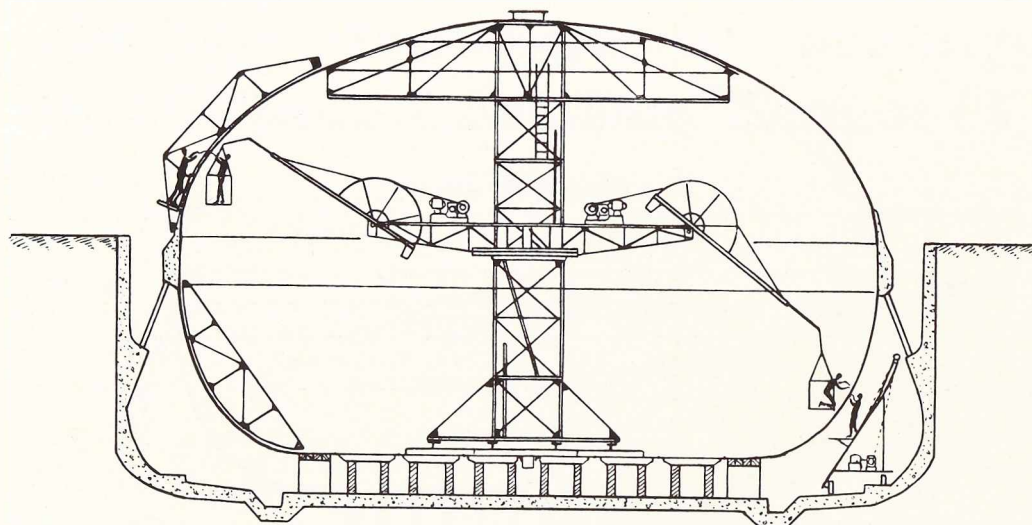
Schéma des dispositifs de soudage en montage.
